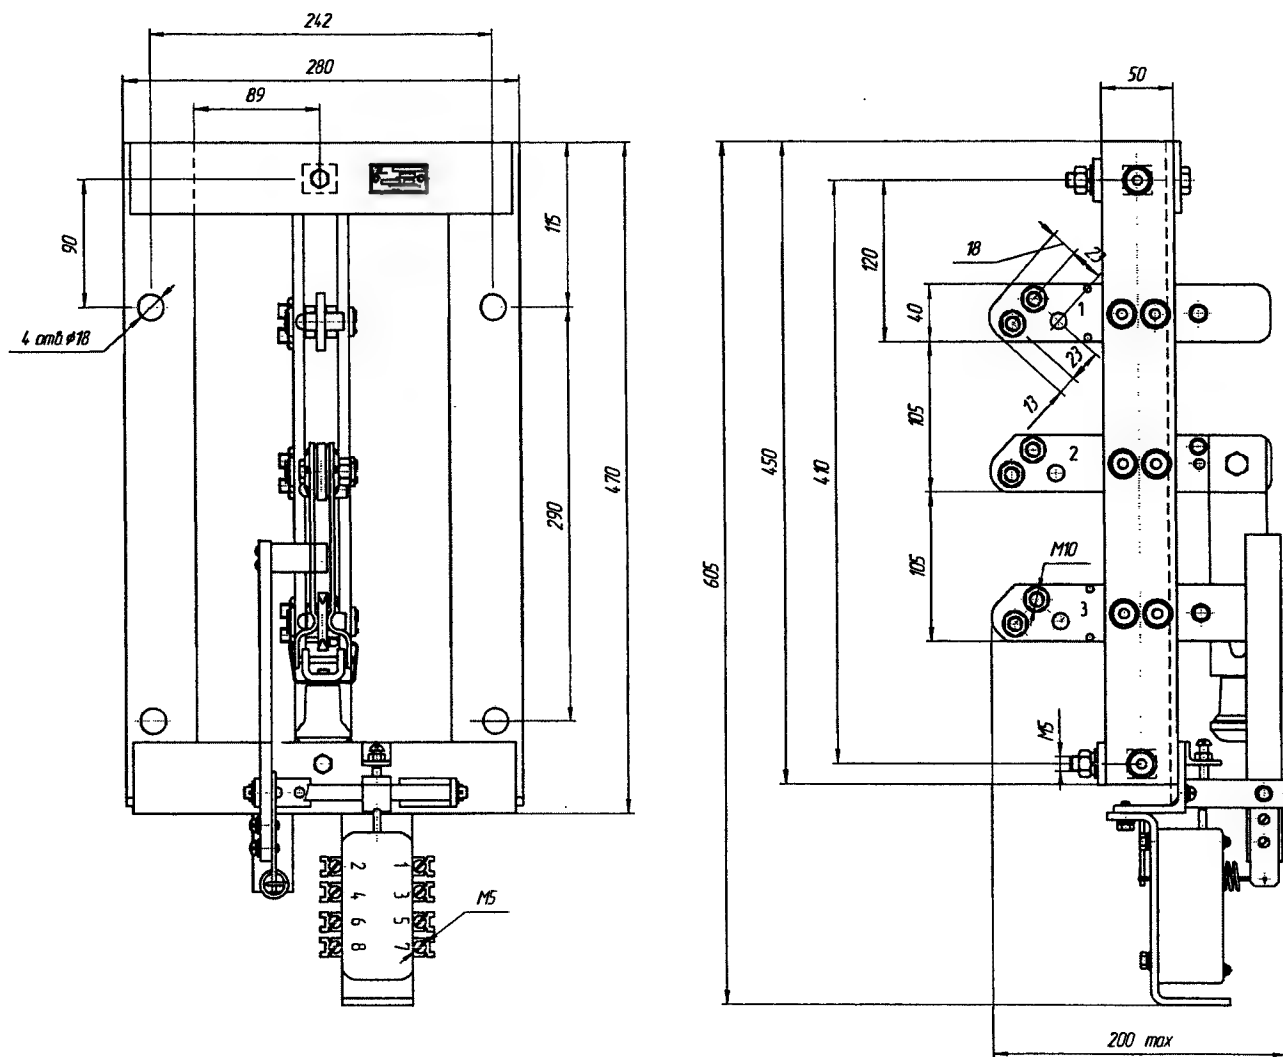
Габаритные, присоединительные и установочные размеры
